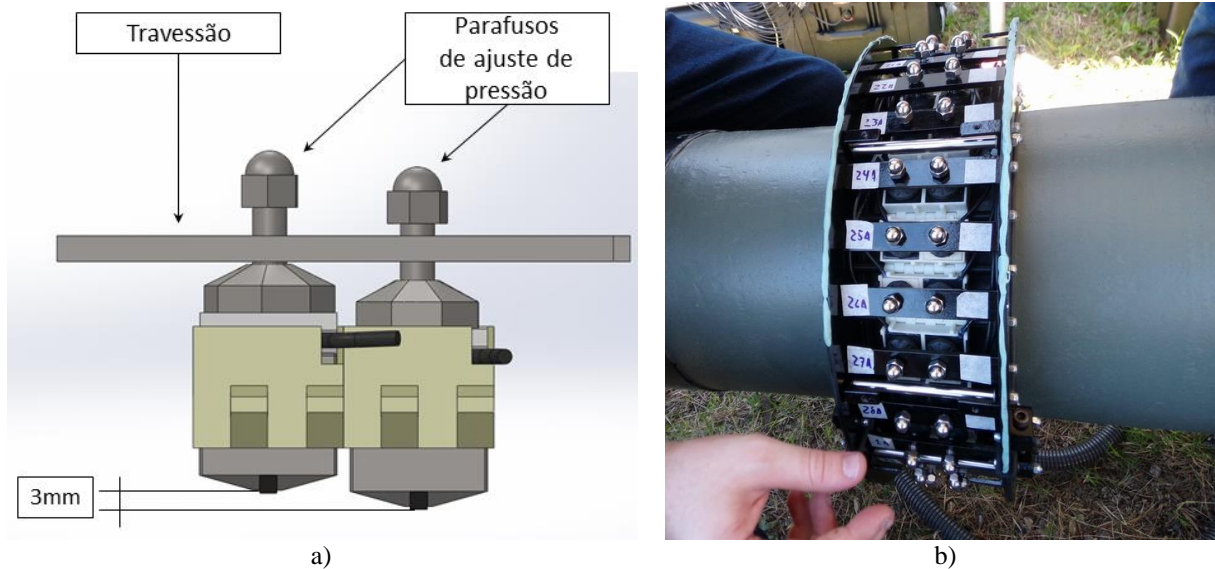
Detalhe da cadeia de suportes de sensores: a) encaixe das duas metades na extremidade das cadeias e b) Foto da construção do colar.
